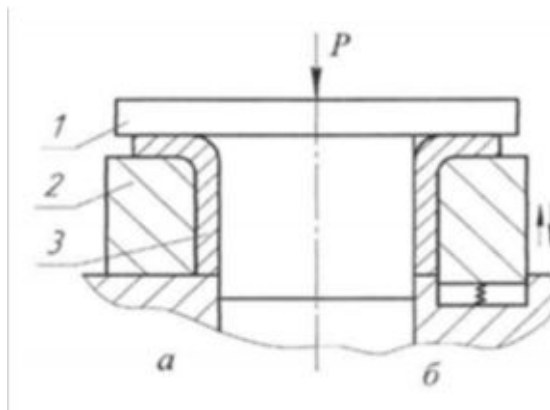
Схема раздачи (а) и осадки (б) трубной заготовки: 1 – пуансон; 2 – матрица; 3 – заготовка
